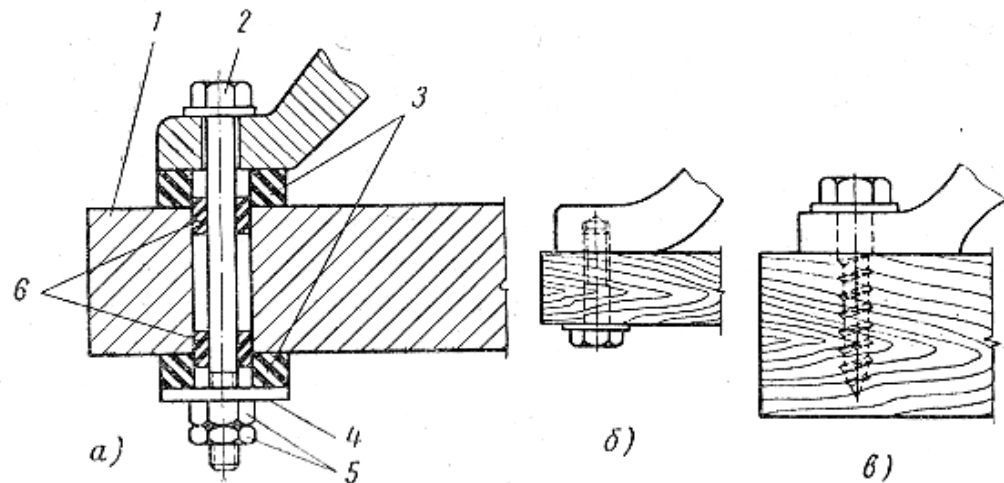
Крепление опорных лап оборудования к крышкам производственных столов и площадок, установленных на кронштейнах:
